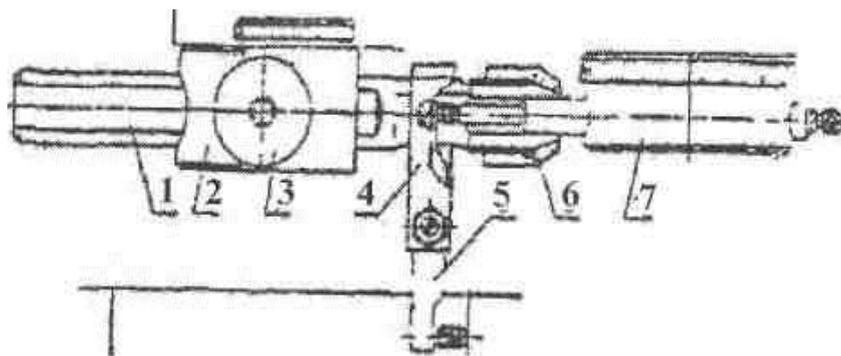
Установка блока для расточки по приспособлению с индикатором:
